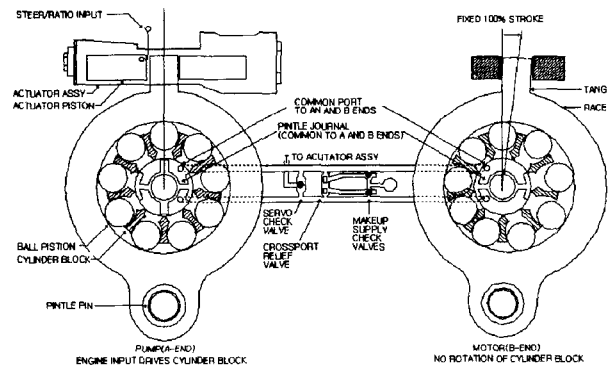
Radial Ball Piston 형의 Pump와 Motor.
